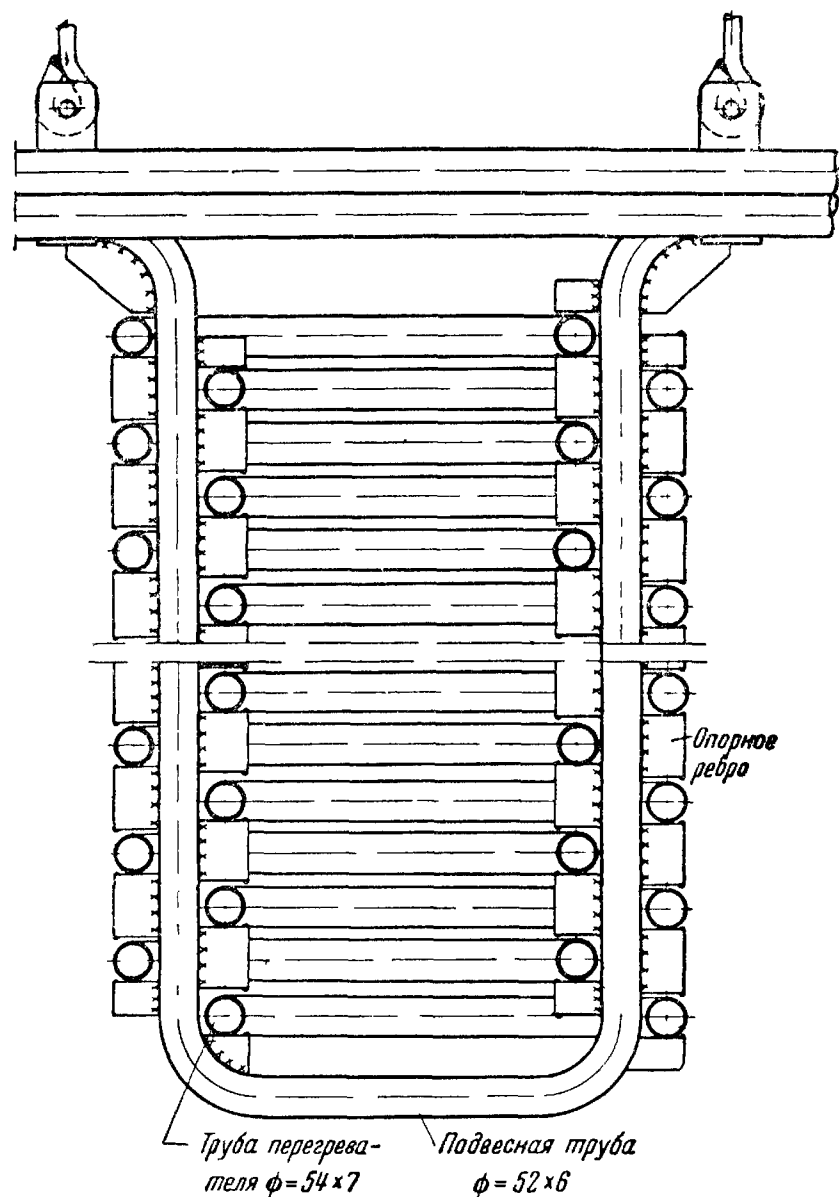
Деталь крепления пароперегревательных труб котла 51СП.
